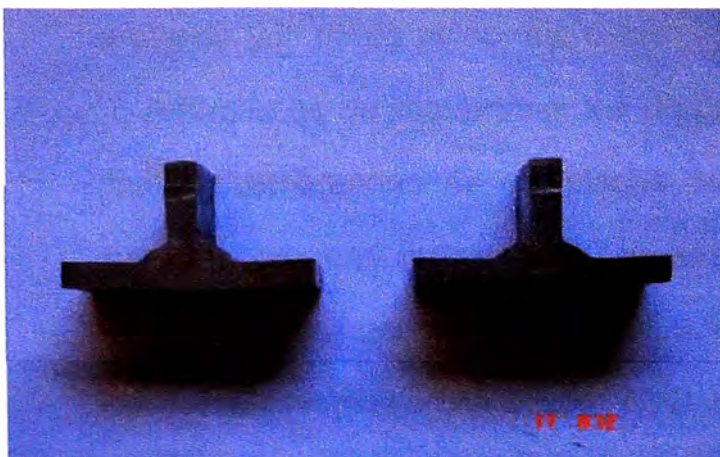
Pruebas De Macroataque Para Soldaduras En Filete
